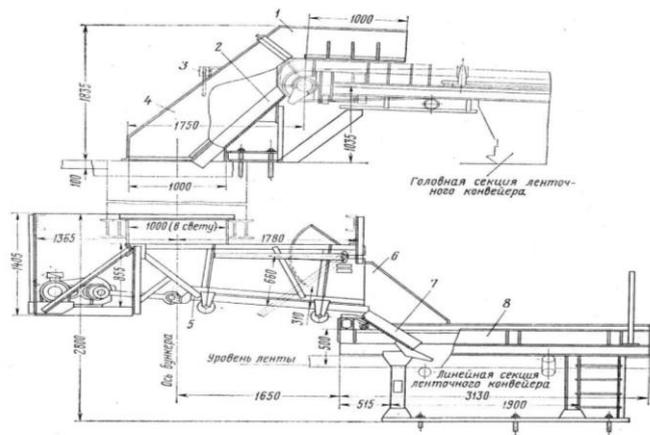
Перегрузочное устройство с конвейера на конвейер на пересекающихся горизонтальных выработках с бункерной перегрузкой
